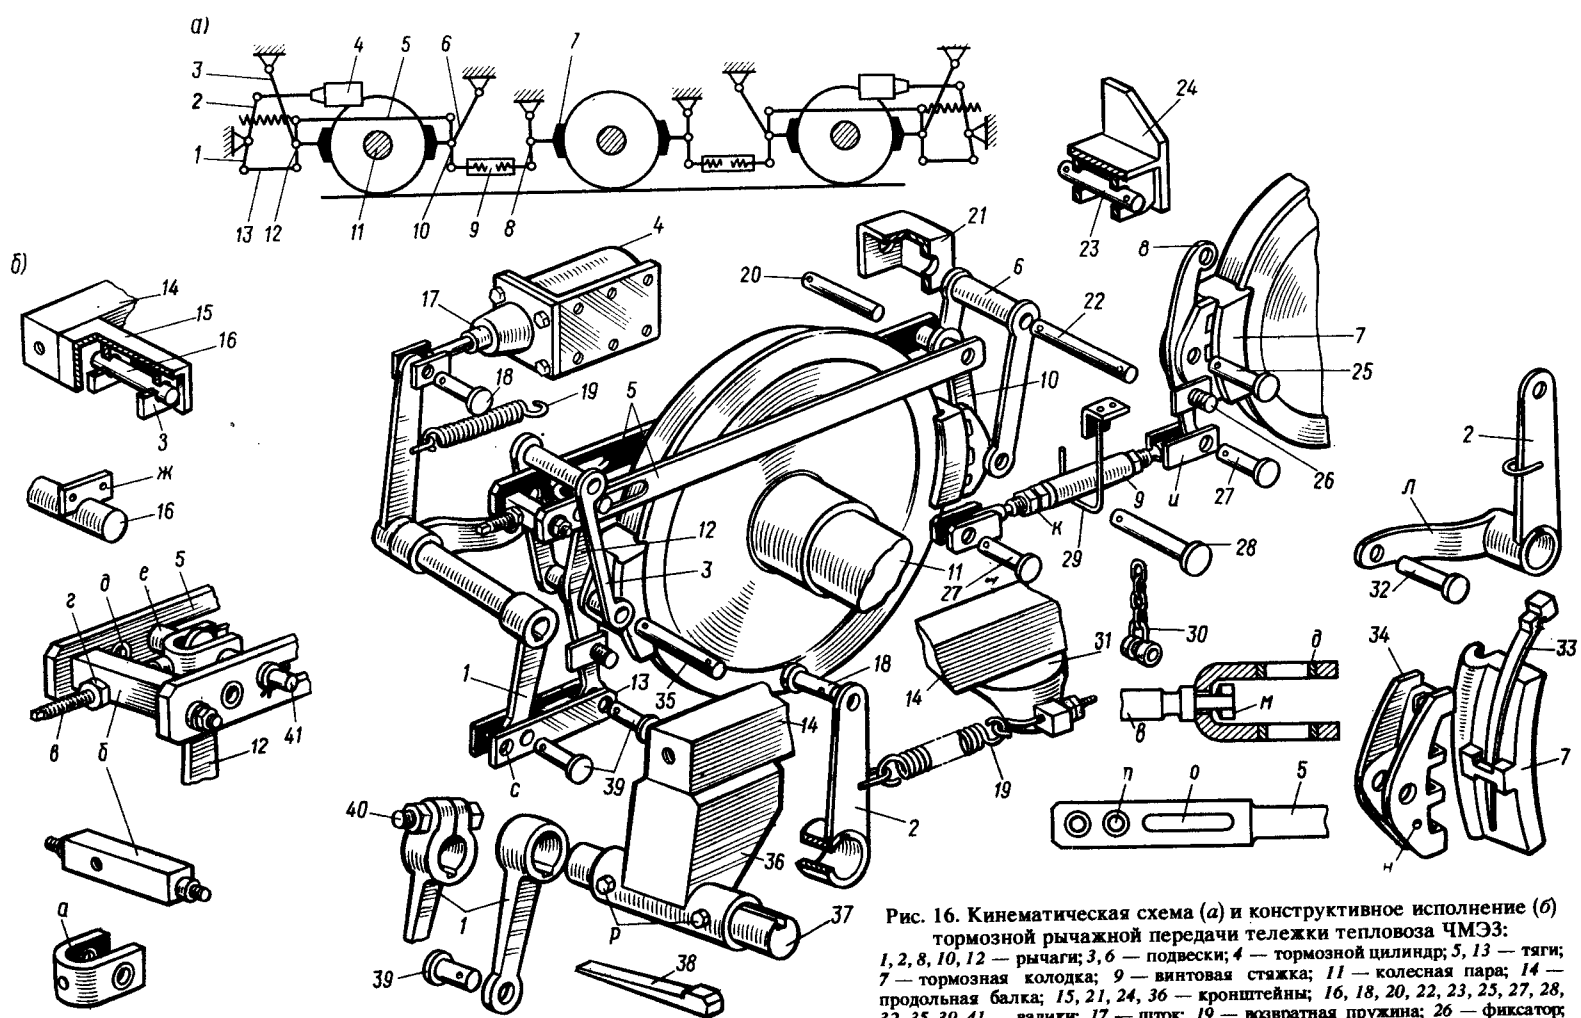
Кинематическая схема (а) и конструктивное исполнение (б) тормозной рычажной передачи тележки тепловоза ЧМЭЗ:
